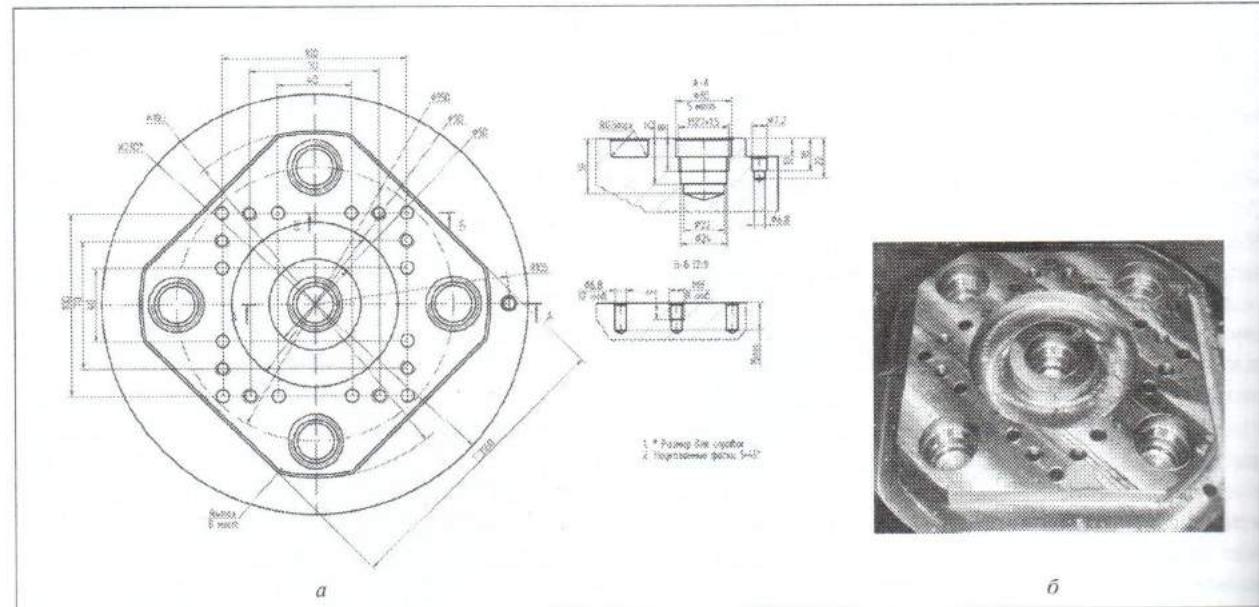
Чертеж (а) и внешний вид (б) тестовой детали
